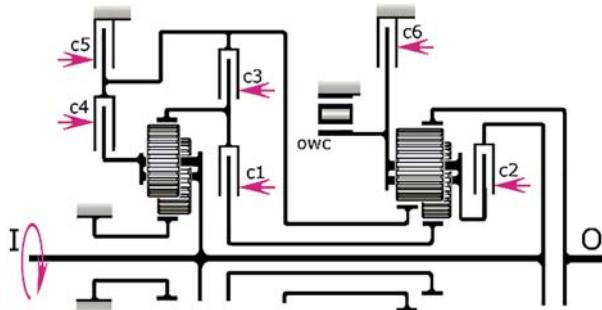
Кинематическая схема 8-ми ступенчатой планетарной коробки передач фирмы Toyota:
